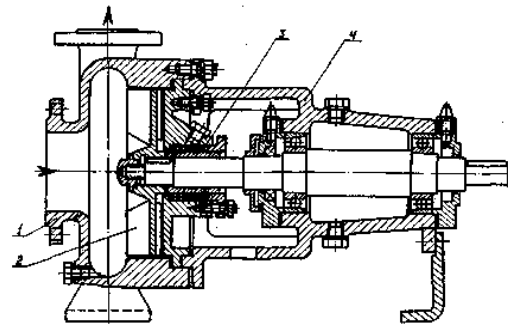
Конструкція насоса ВВН: 1 – корпус; 2 – робоче колесо; 3 – ущільнення кінцеве; 4 – корпус підшипників
